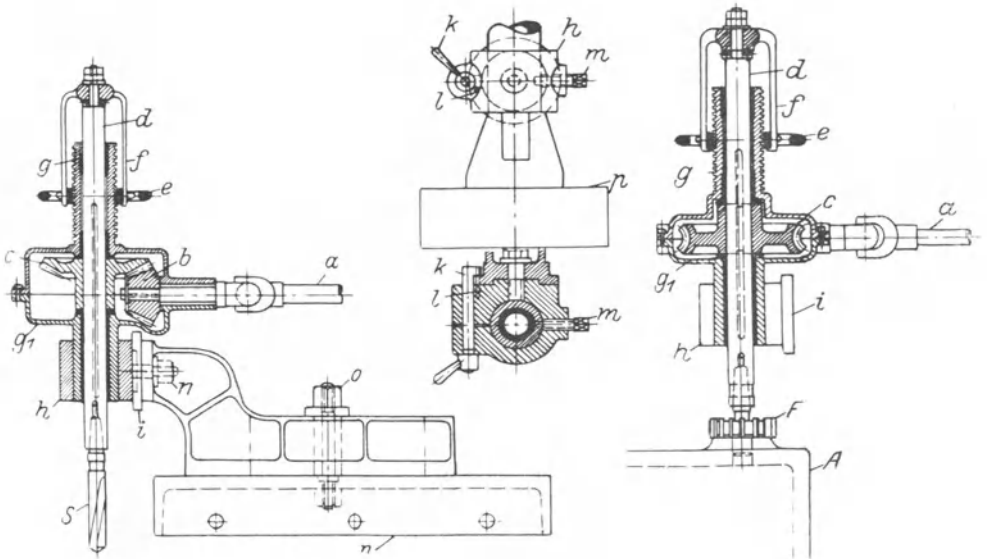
Bohrvorrichtung für schwer transportierbare Arbeitsstücke.
